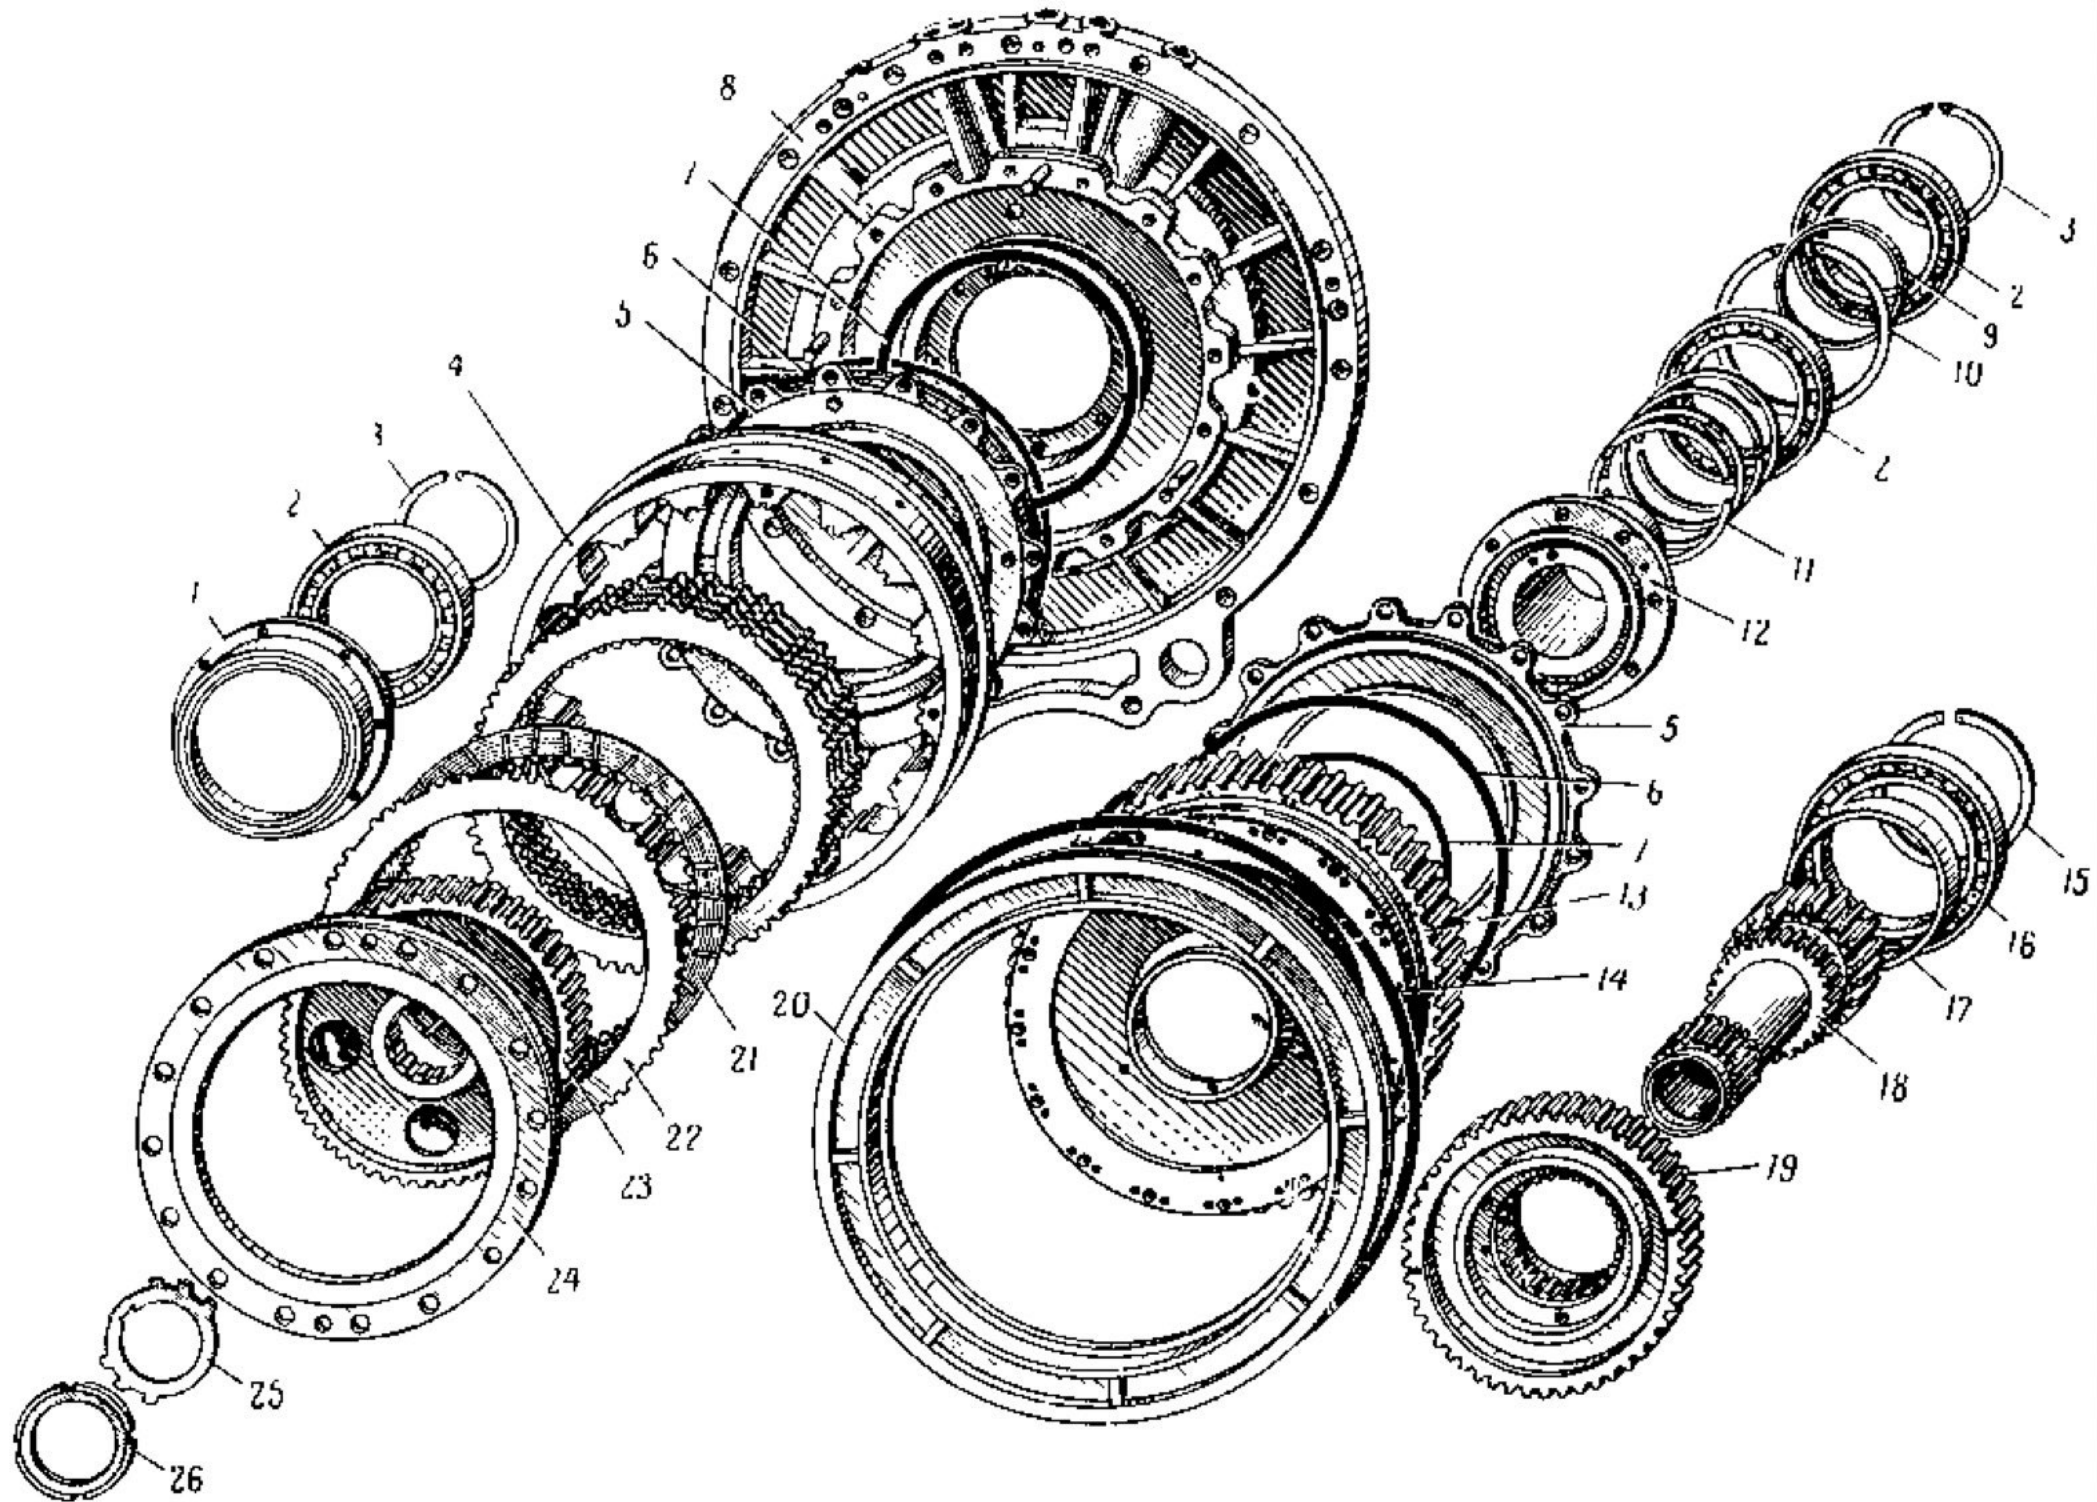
Промежуточный вал с картером и манетарпом коробки передач
